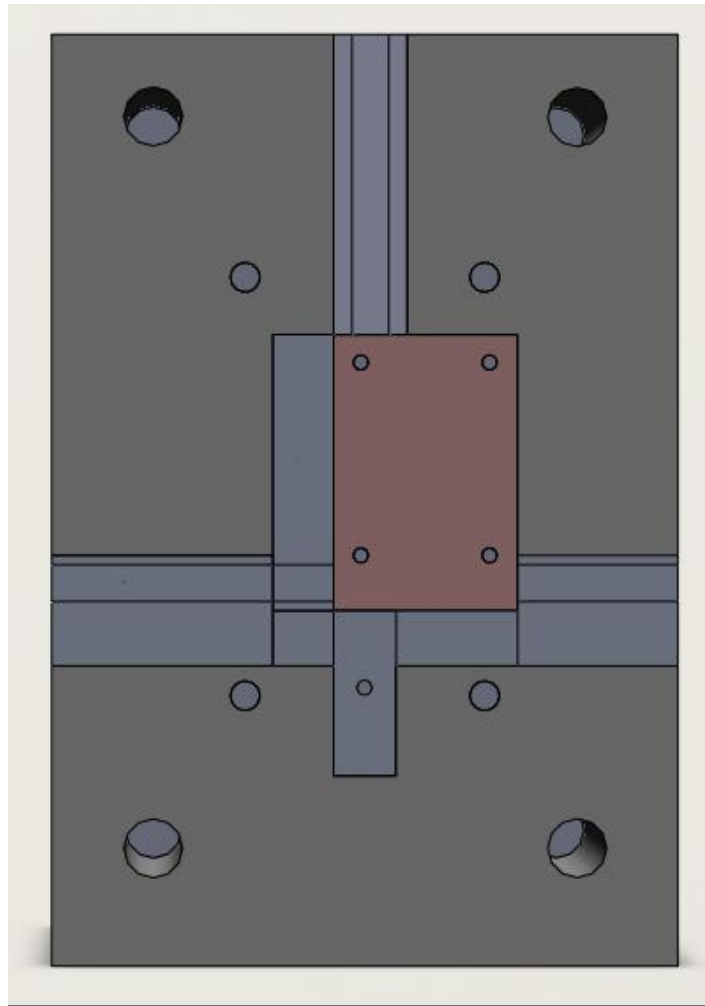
Vista en planta de la configuración de llenado por pared largo.
